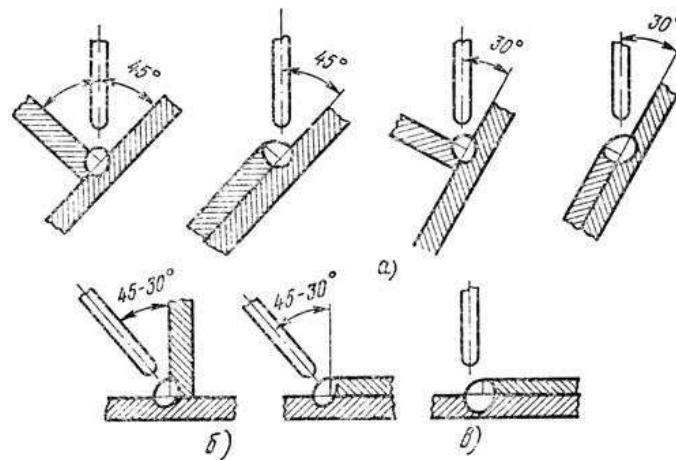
Способы выполнения угловых, тавровых и нахлесточных швов: а - сварка в симметричную и несимметричную 'лодочку', б - наклонным электродом, в - сварка с оплавлением кромки
